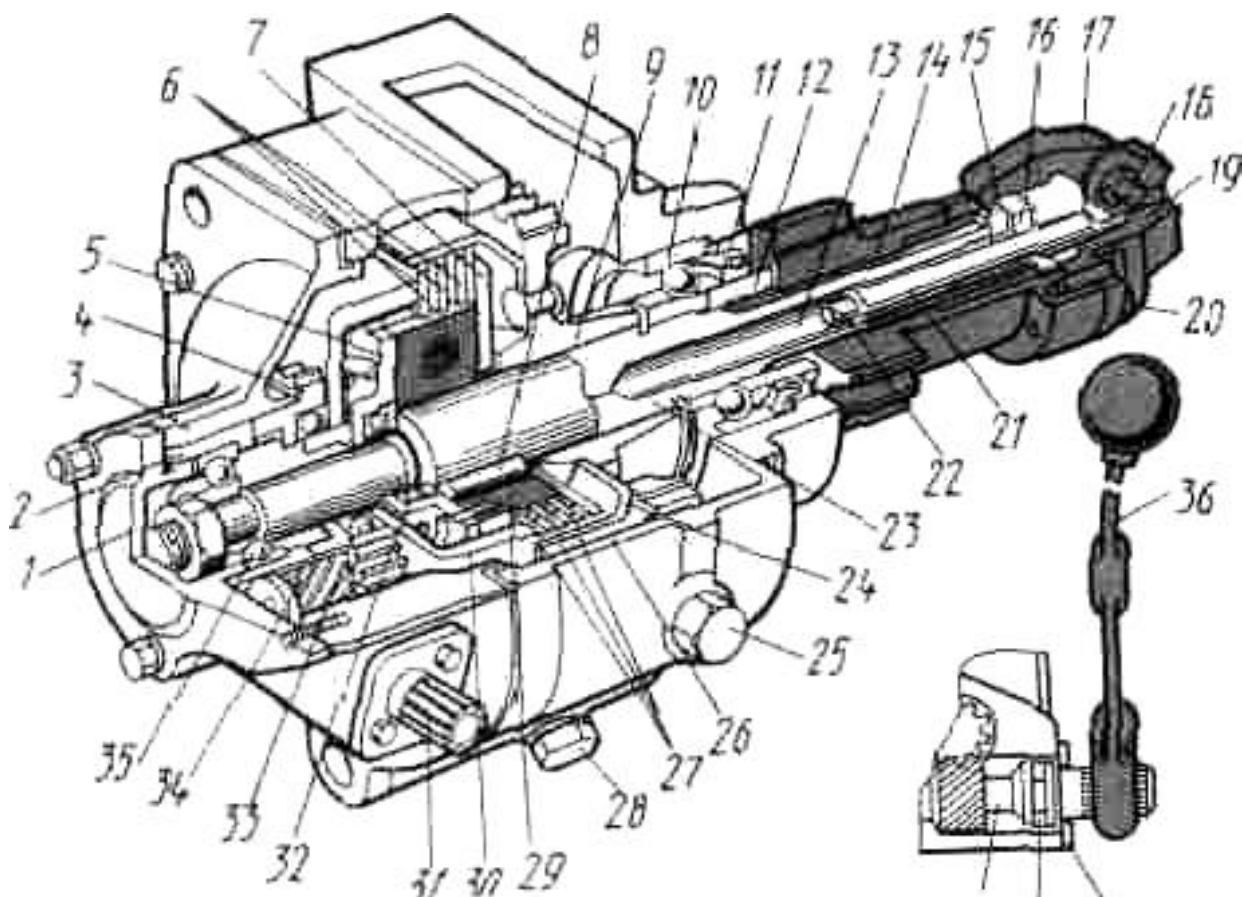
Редуктор РПД1.000М пускового двигателя П-10УД
